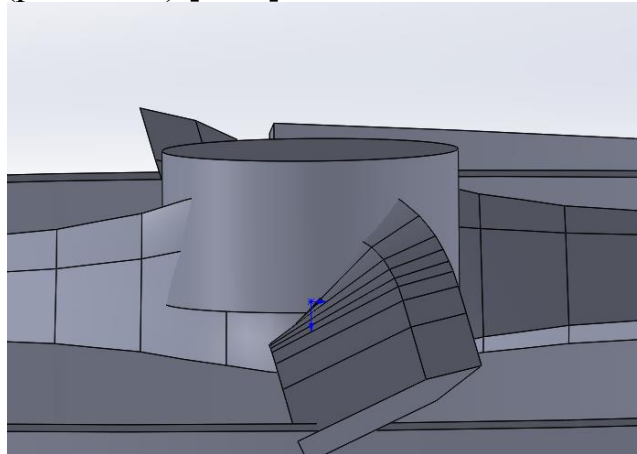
Вид сбоку на ножевой исполнительный орган геохода
